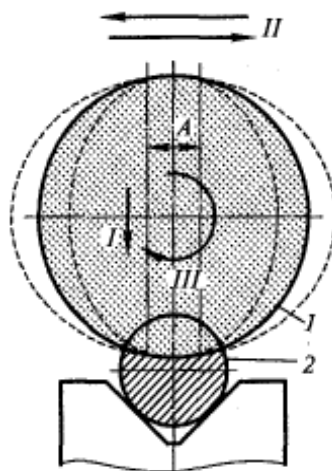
Схема роботи абразивно-відрізного верстата:
